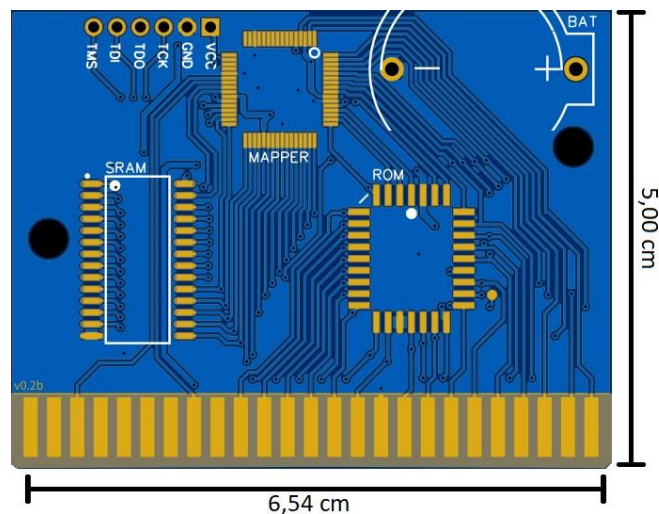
PCB Final com dimensões de 6,54 x 5,00cm
